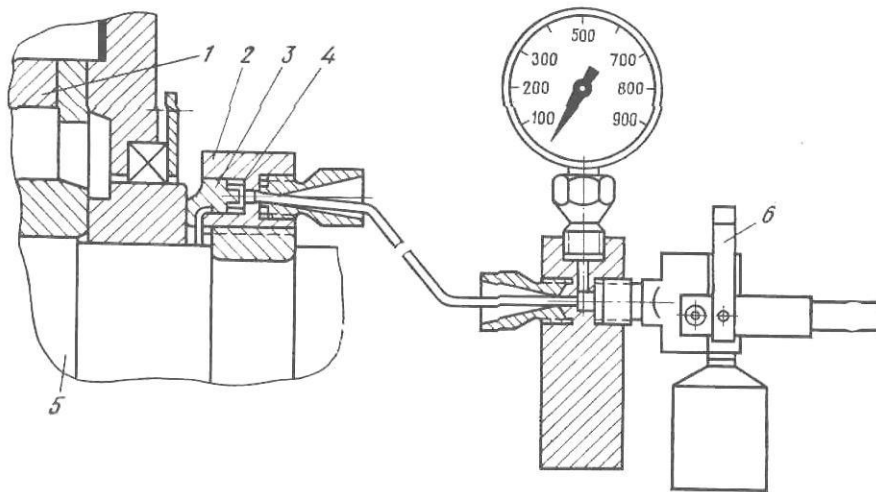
Напрессовка роликового подшипника, имеющего внутреннее конусное отверстие, на конусную шейку валка при помощи гидравлической гайки
